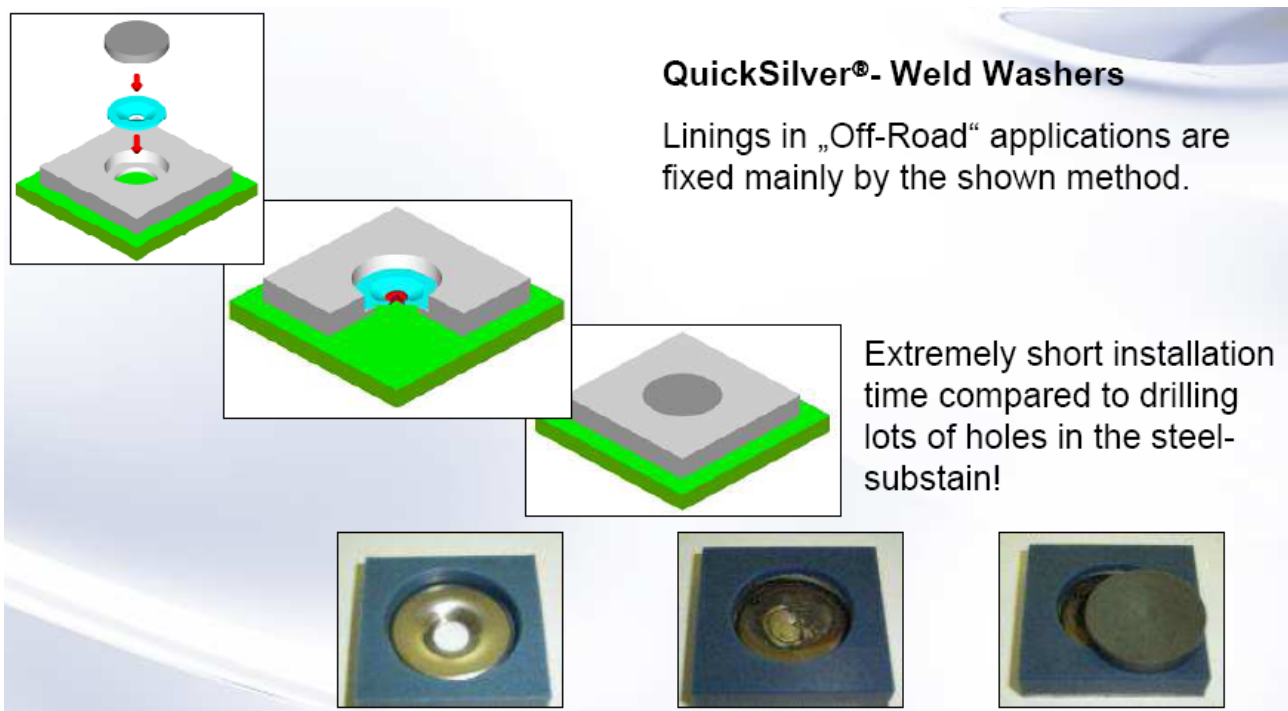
Dimostrazione della facilità di montaggio in opera con il metodo QuickSilver®-Weld Washers.
